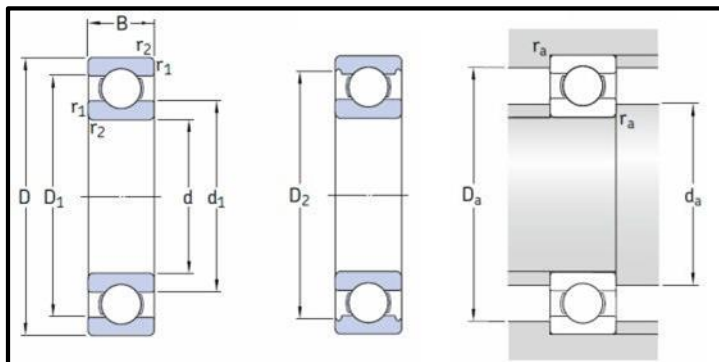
diseño y medidas del rodamiento rígido 61805.
